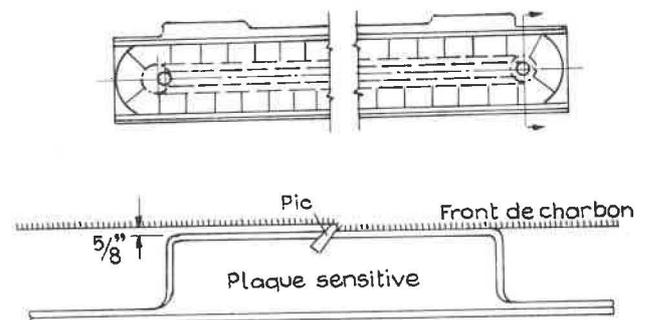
Infrastructure rigide avec les deux plaques sensibles. En dessous, vue détaillée du jeu créé par le pic en avant de la plaque sensible.
